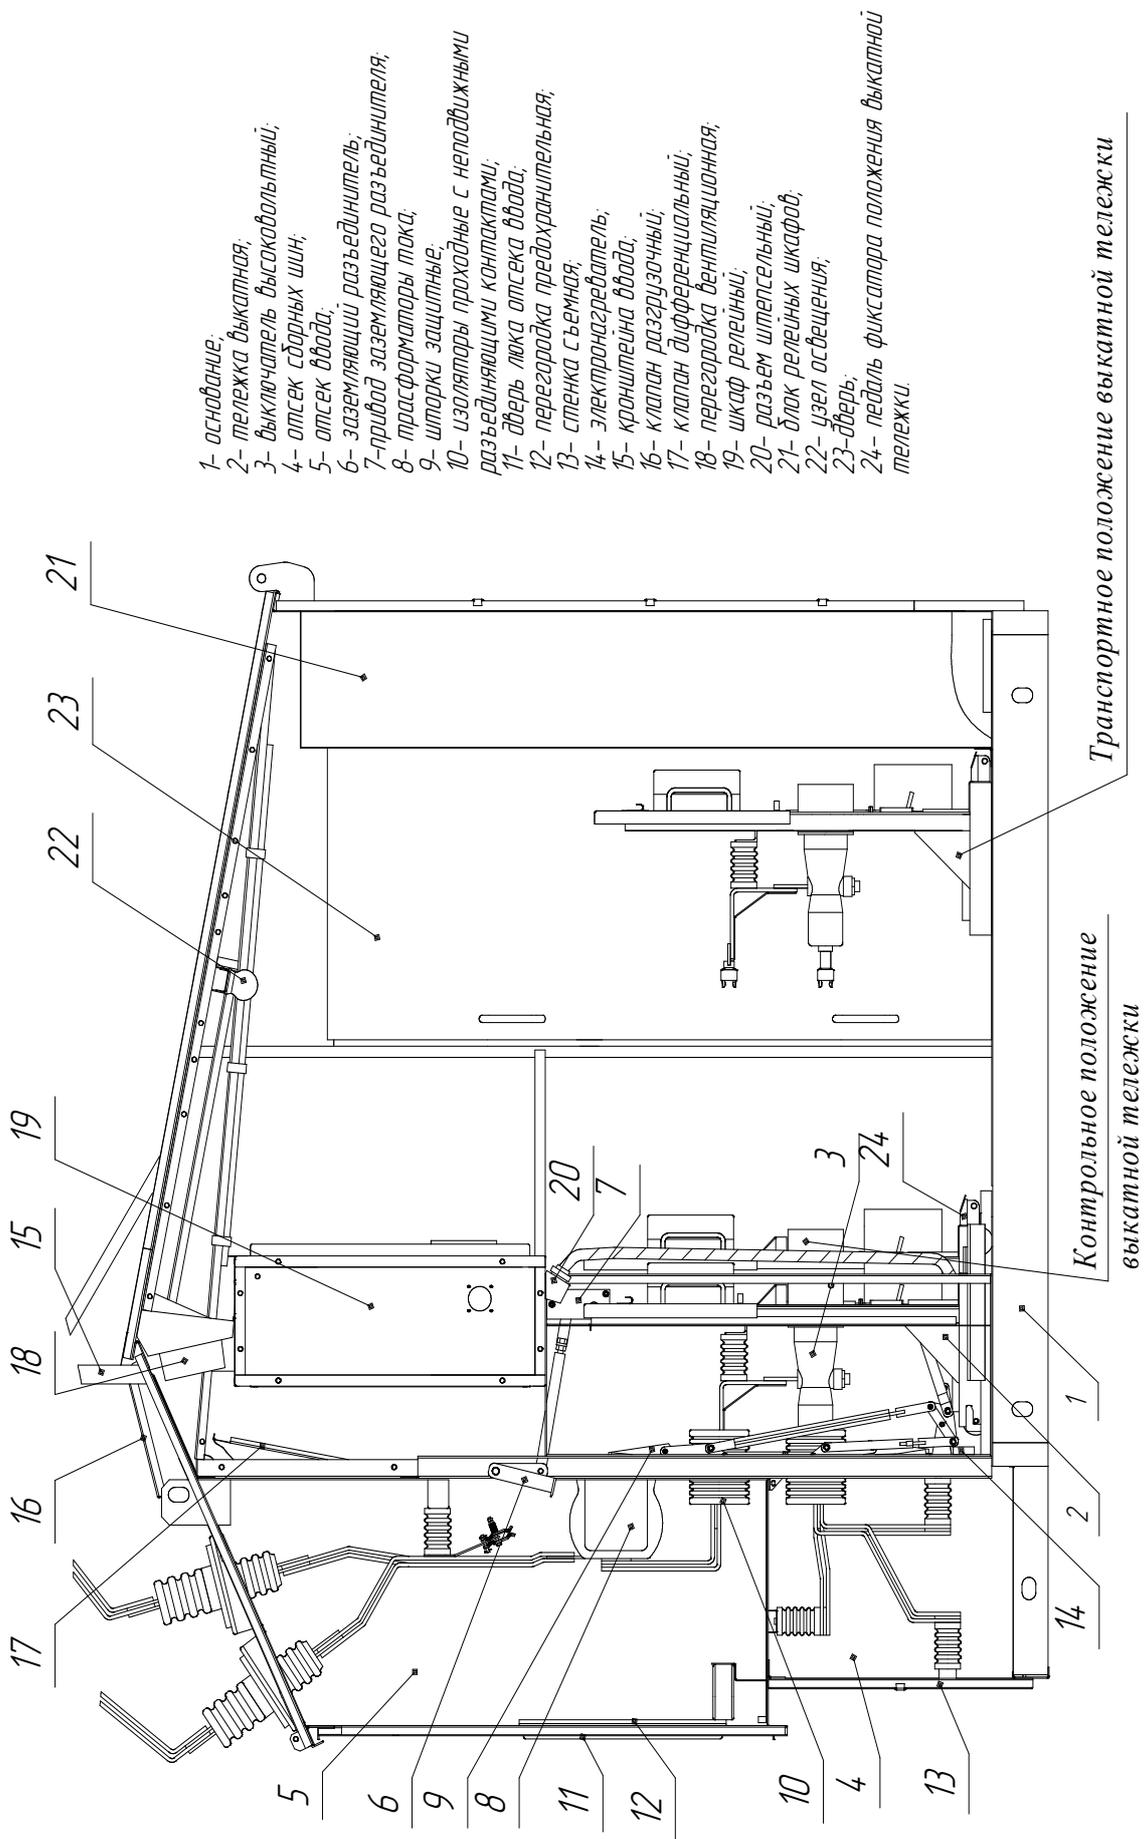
Блок КРУН исполнения У1 (Разрез по ячейке на 1600 А с воздушным вводом (выводом))
